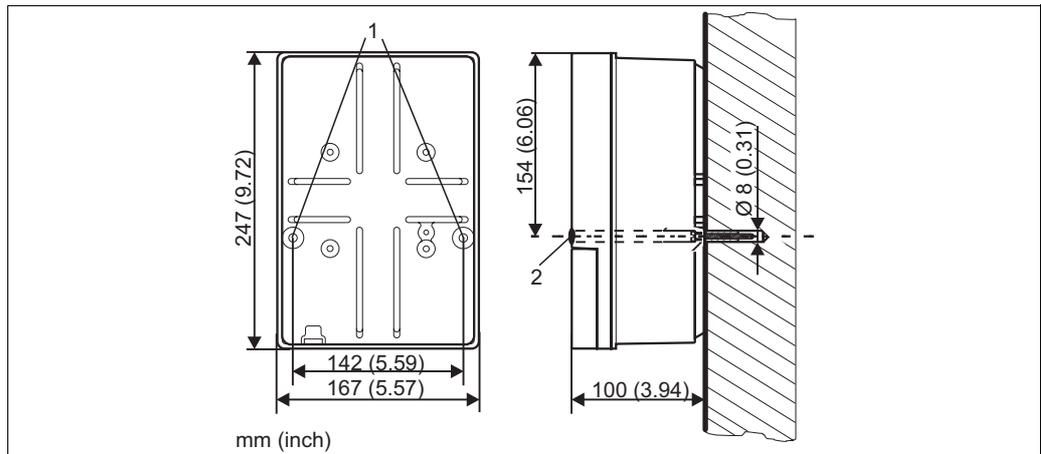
Maße für die Wandmontage, Befestigungsschraube: \varnothing 6 mm (0,24"), Dübel: \varnothing 8 mm (0,31")
